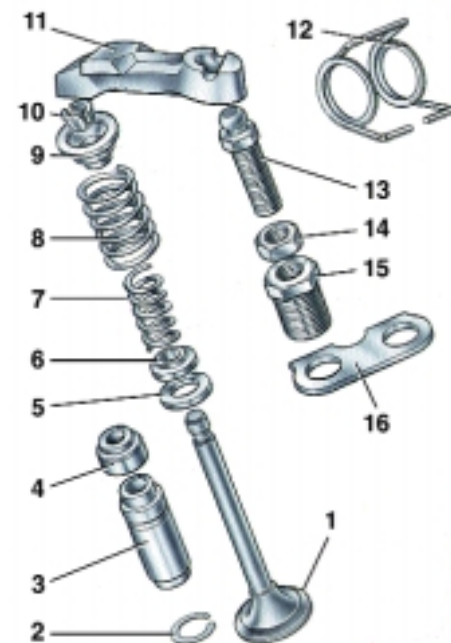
Детали клапанного механизма двигателя мод. 2106-70: 1 – клапан; 2 – стопорное кольцо; 3 – направляющая втулка; 4 – маслоотражательный колпачок; 5 – опорная шайба наружной пружины; 6 – опорная шайба внутренней пружины; 7 – внутренняя пружина; 8 – наружная пружина; 9 – тарелка пружины; 10 – сухари; 11 – рычаг привода клапана; 12 – пружина рычага; 13 – регулировочный болт; 14 – контргайка регулировочного болта; 15 – втулка регулировочного болта; 16 – стопорная пластина пружины рычага
